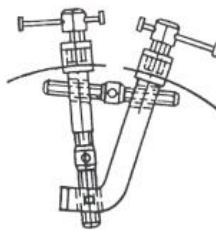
Пристрій установки для складання поздовжніх стиків корпусу обичайки
